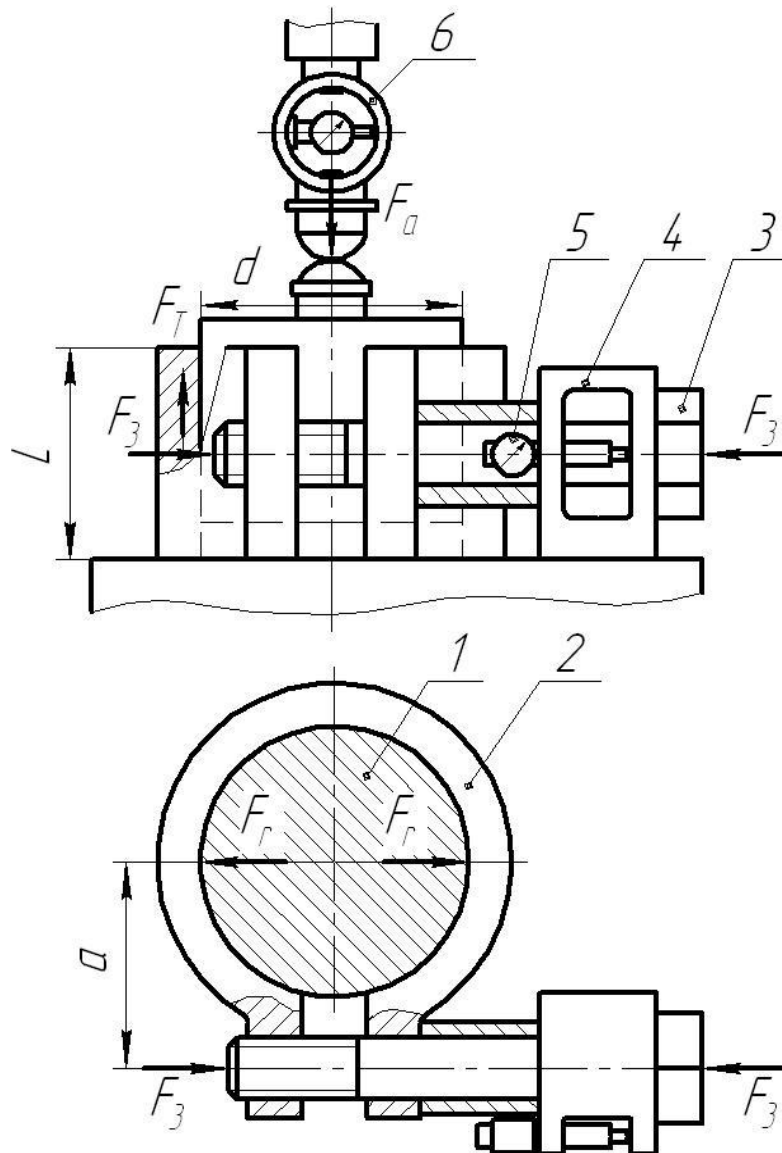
Схема клемового з'єднання лабораторної установки, розміщеного на робочому столі преса ДМ30М
